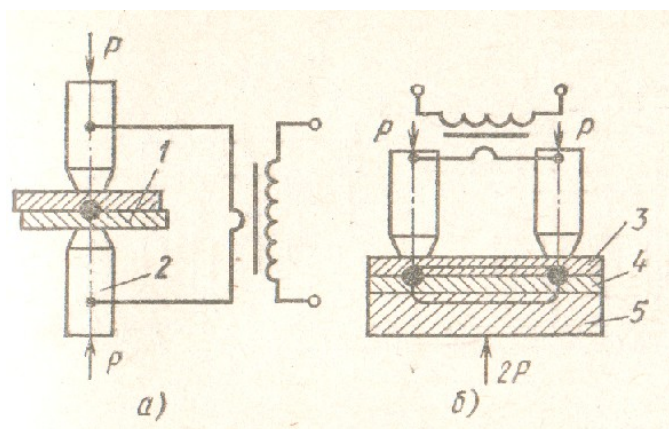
Схема контактной точечной сварки: а – двусторонней; б – односторонней.
